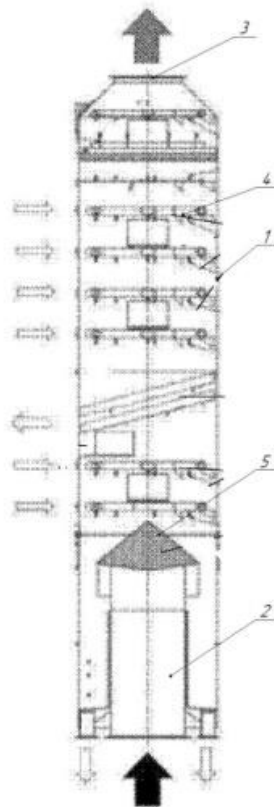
Конструкція кожухотрубного теплообмінника
